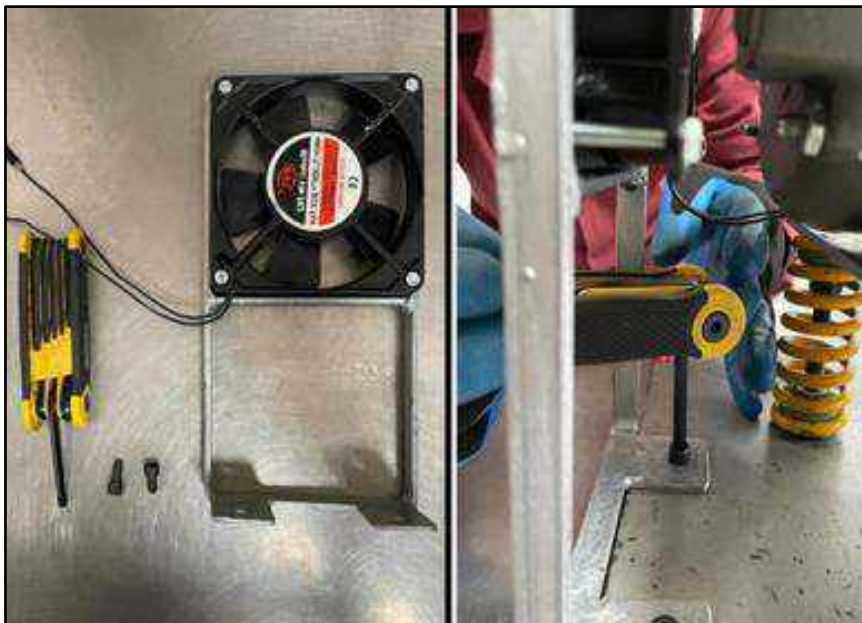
Ajuste del motor a la placa de resortes
